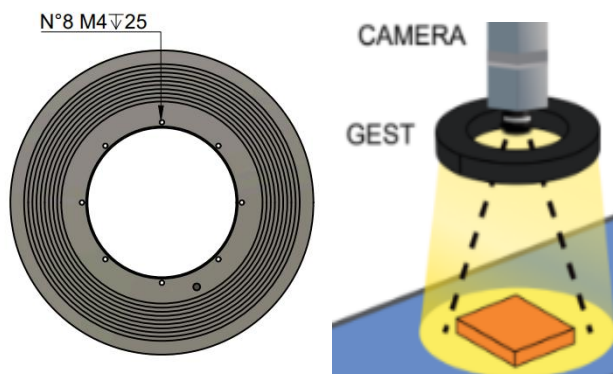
Fissaggio e assemblaggio illuminatore - telecamera
